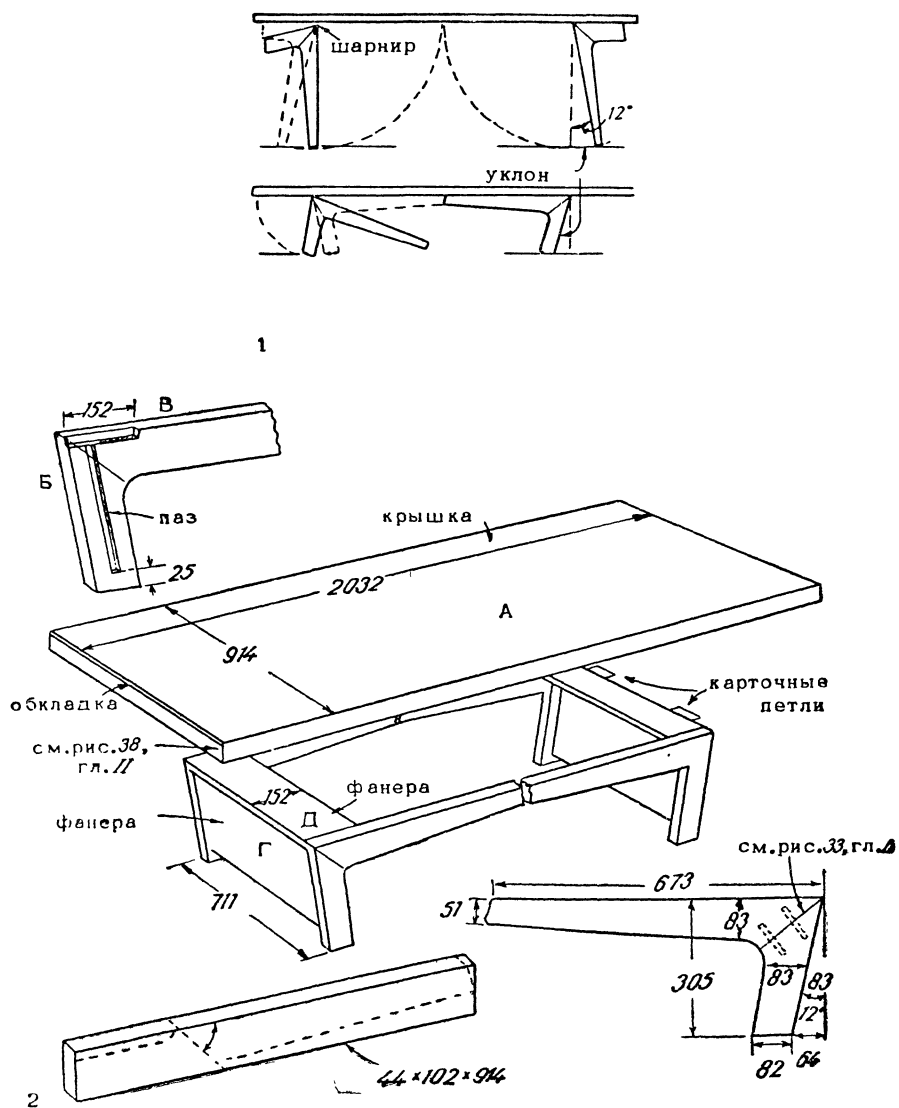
2. 1 — варианты положения ножек стола; 2 — эскиз сборки стола.
